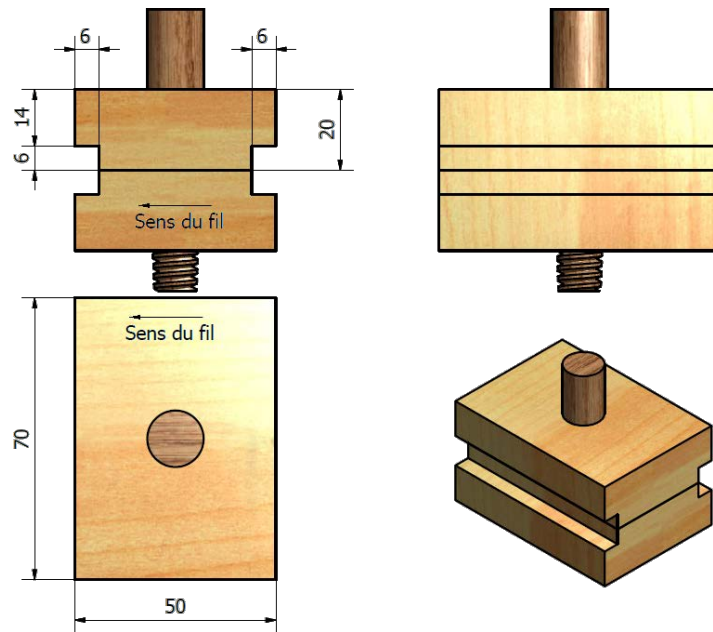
Plan des éprouvettes d'essais d'arrachement
